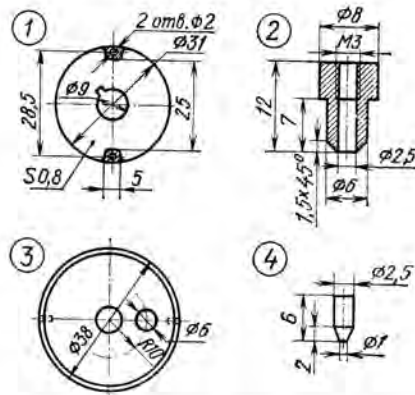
Детали дополнительного токосъемника: 1 — шайба; 2 — щеткодержатель; 3 — доработка подшипникового щита; 4 — щетка.
